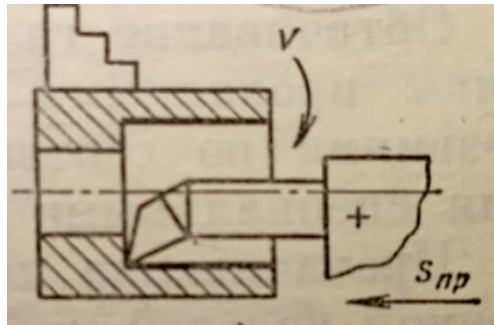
Схема розточування отвору на токарно-гвинторізному верстаті.
